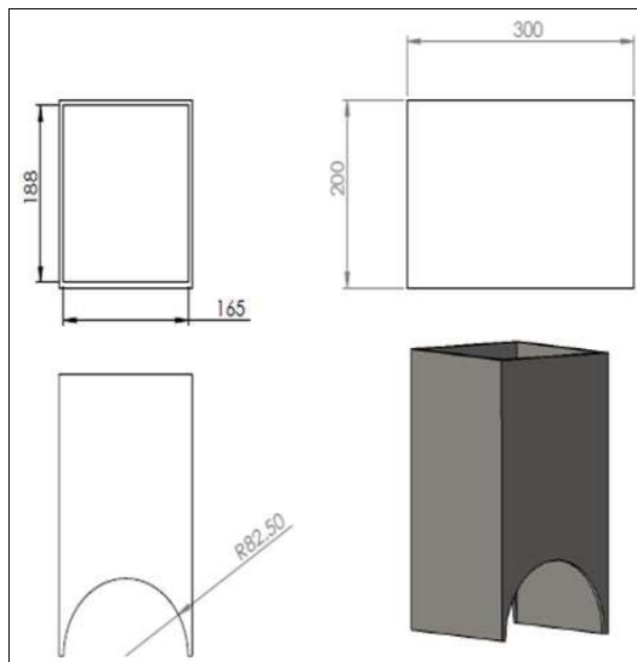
Dimensiones de la tolva, con las medidas en mm. Fuente: (Arroyo, 2016)
